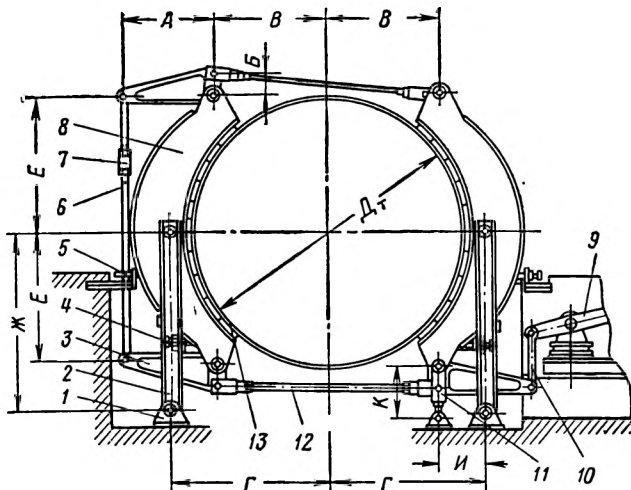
Исполнительный орган тормоза машин НКМЗ
